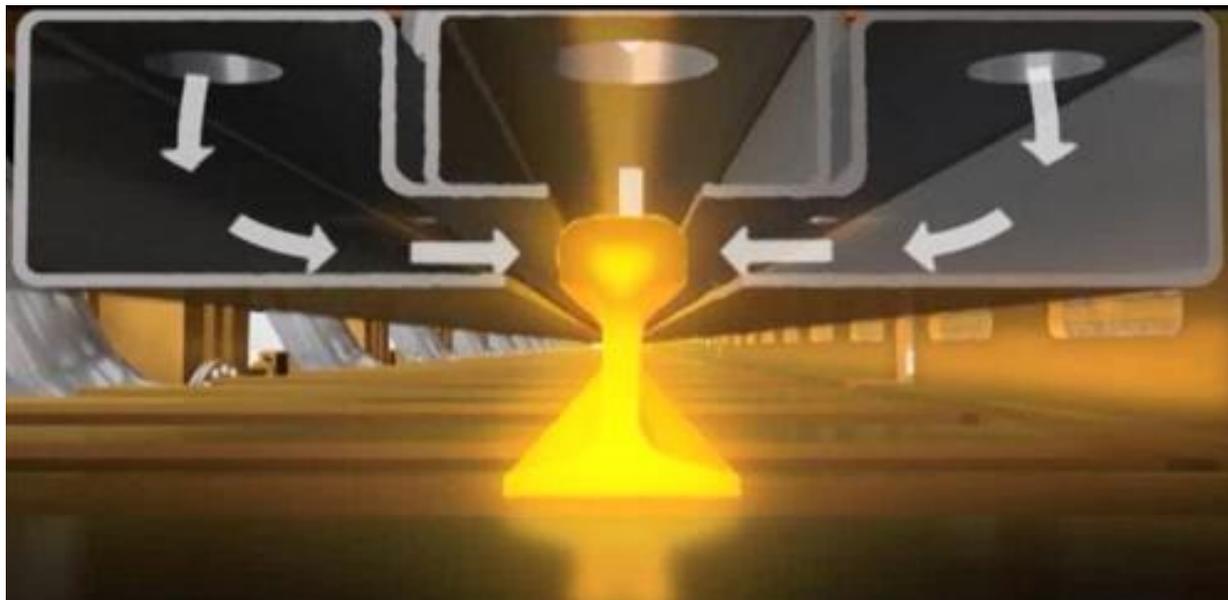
Общая схема термической обработки рельсов воздухом с прокатного нагрева
